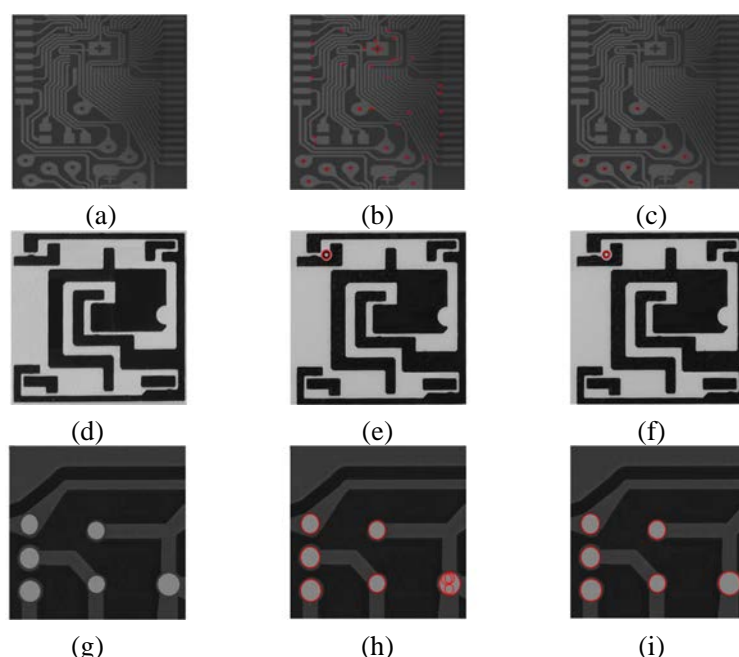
PCB 裸板图像导孔检测实例图: (a) PCB1 输入图像; (b) PCB1 霍夫; (c) PCB1 本文方法; (d) PCB2 输入图像; (e) PCB2 霍夫; (f) PCB2 本文方法; (g) PCB3 输入图像; (h) PCB3 霍夫; (i) PCB3 本文方法
